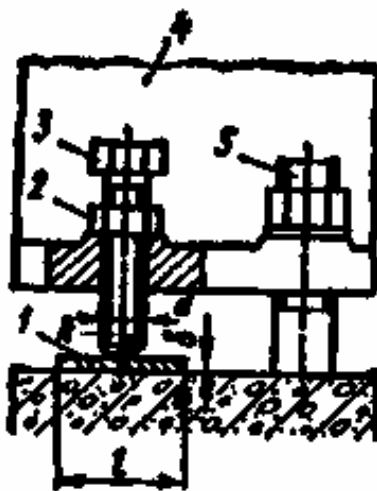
Схема выверки отжимными регулировочными винтами
